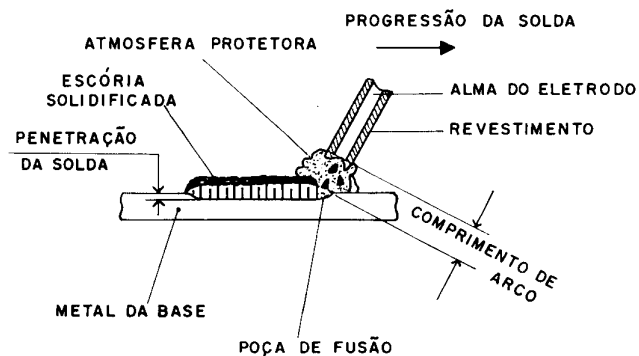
Soldagem por eletrodo revestido (OKUMURA e TANIGUCHI, 1982)
